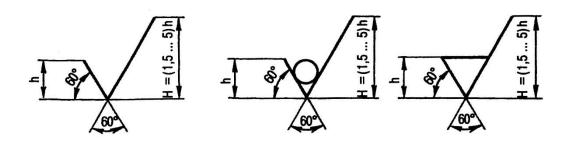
Знаки, применяемые для обозначения шероховатости
